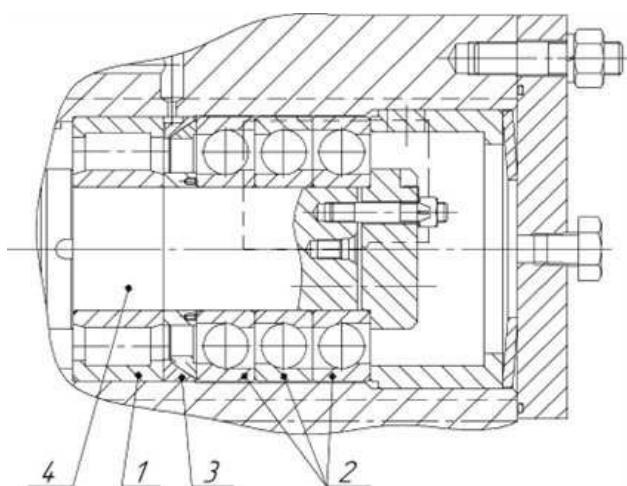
Подшипниковый узел компрессора 8ГВ
